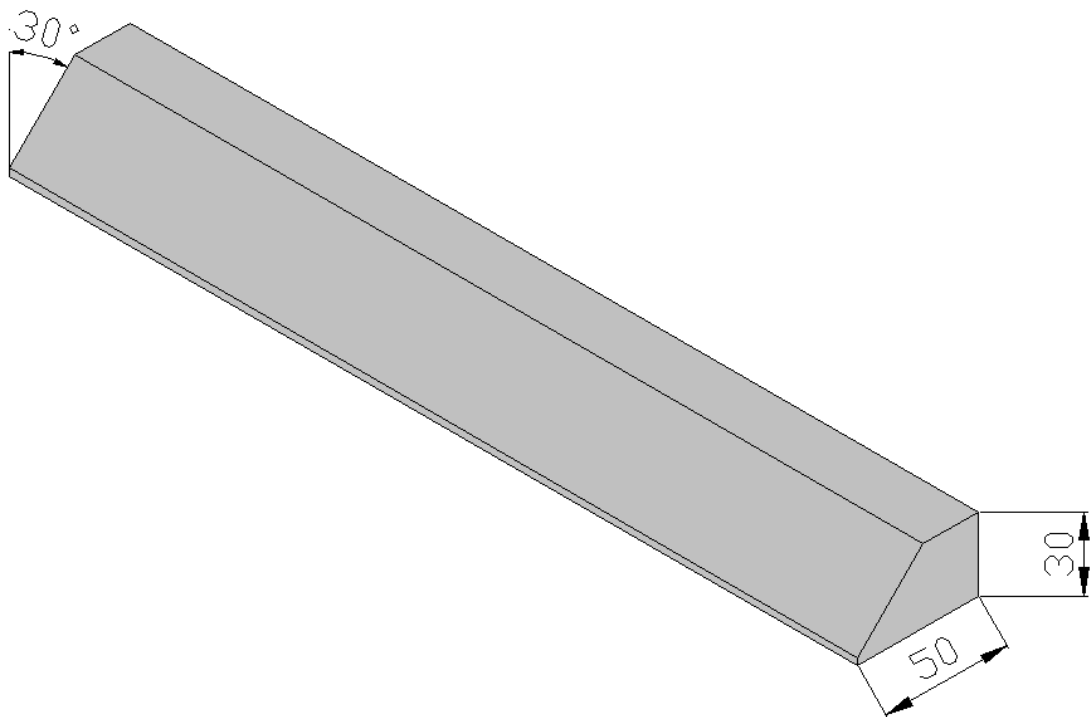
Probeta de la junta FMSB-DI-WPS-02 para ensayos de consumo en soldadura
